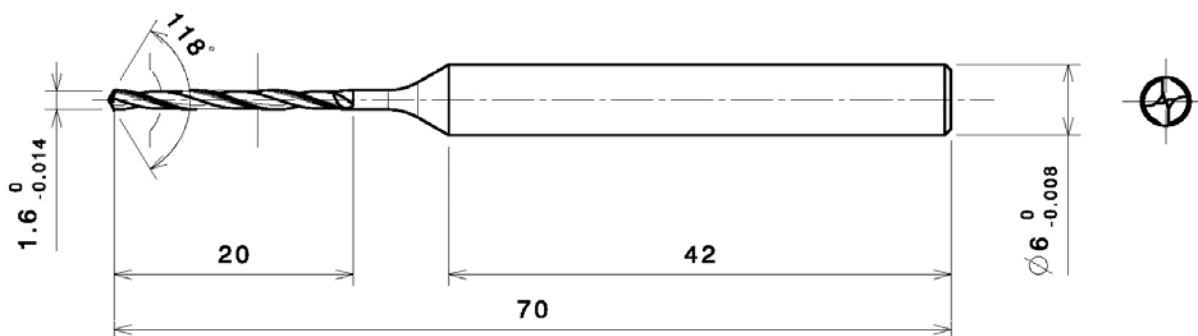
Чертеж твердосплавной фрезы SSD D1.6X20FX 70-6 из сплава UF10
